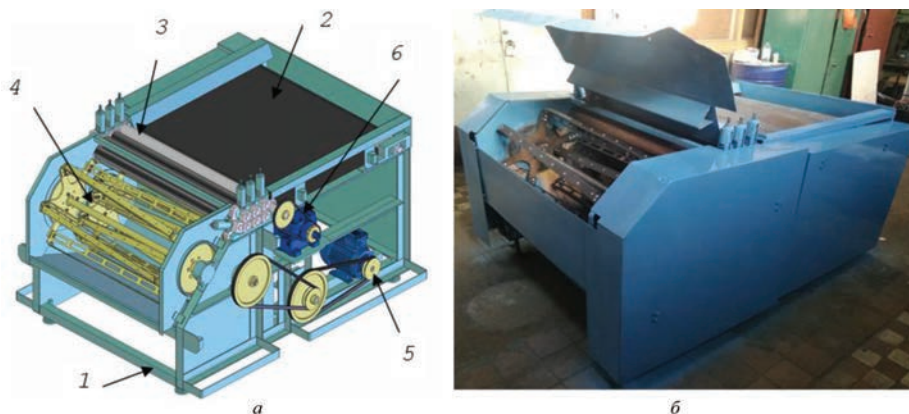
Макетный образец установки трепальной: *а* – 3D модель макетного образца; *б* – общий вид макетного образца:
